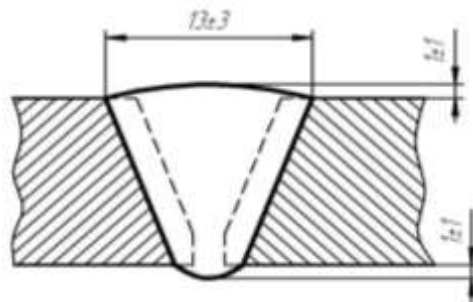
Геометрія зварного шва під час заварювання тріщини
